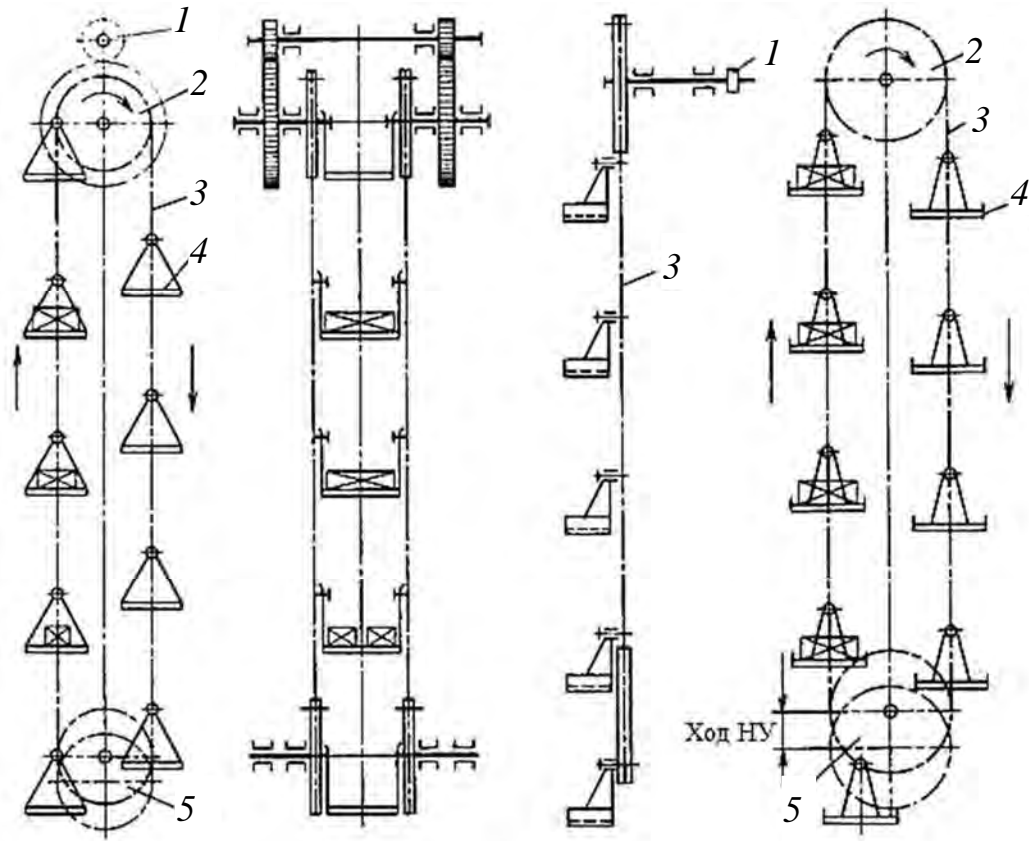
Схема люлочного элеватора (одноцепного и двухцепного): 1 – привод; 2 – приводные звездочки; 3 – тяговые цепи; 4 – люльки; 5 – натяжные звездочки
